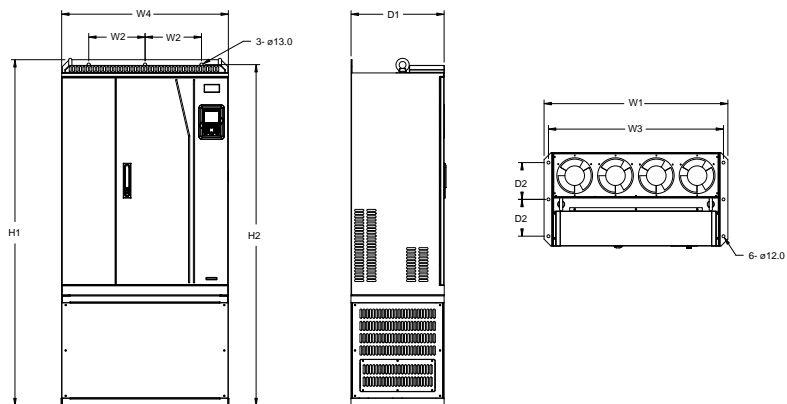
Схема для напольного монтажа ПЧ 660 В, 250 - 355 кВт
